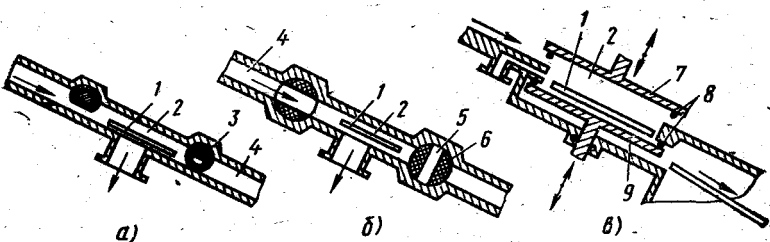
Однокамерные шлюзовые загрузочные устройства:
